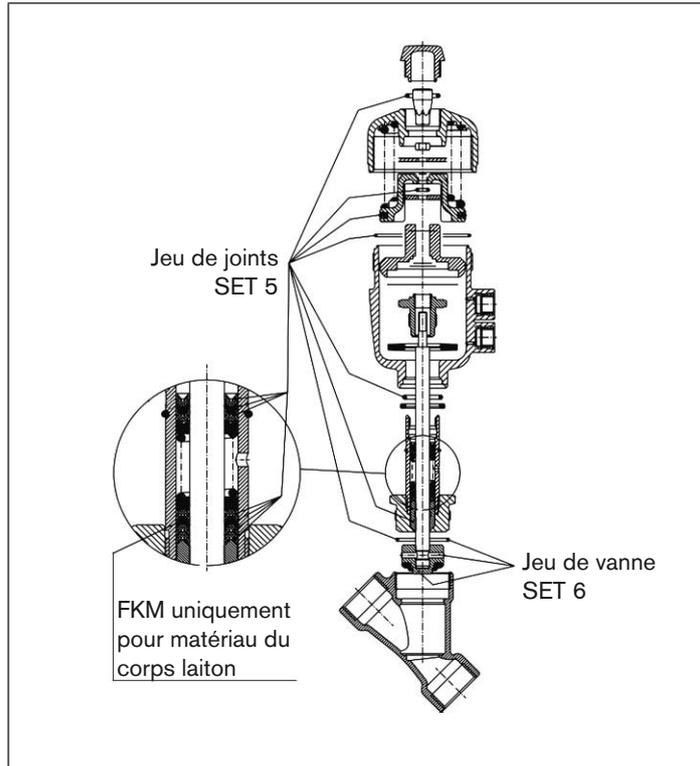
Pièces de rechange pour vanne à siège incliné
